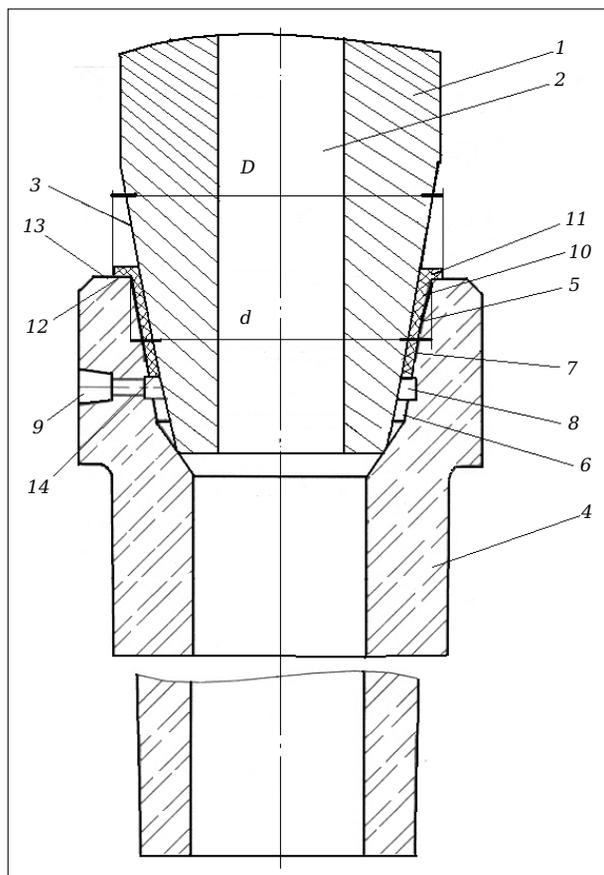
Устройство для защиты струи металла при разливке на МНЛЗ
